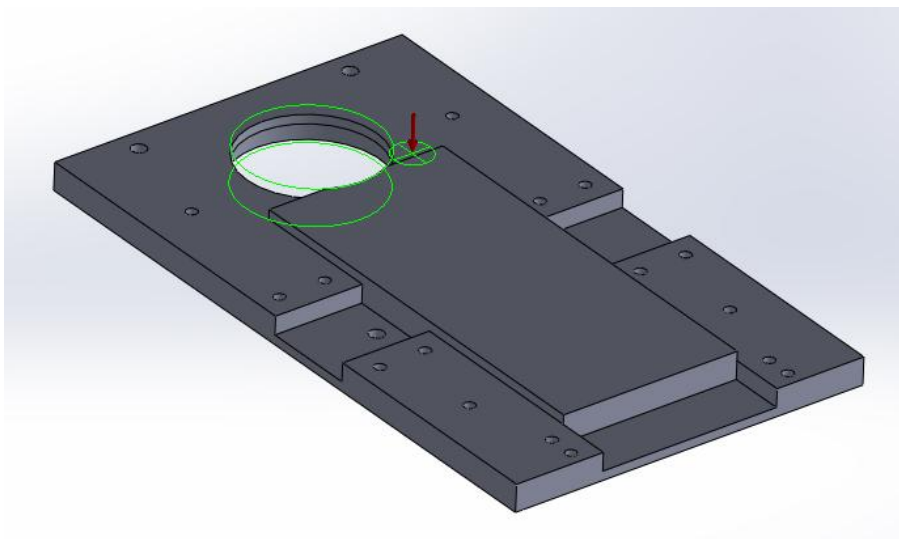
Rasgo de agujero del pistón de la parte fija del molde.
